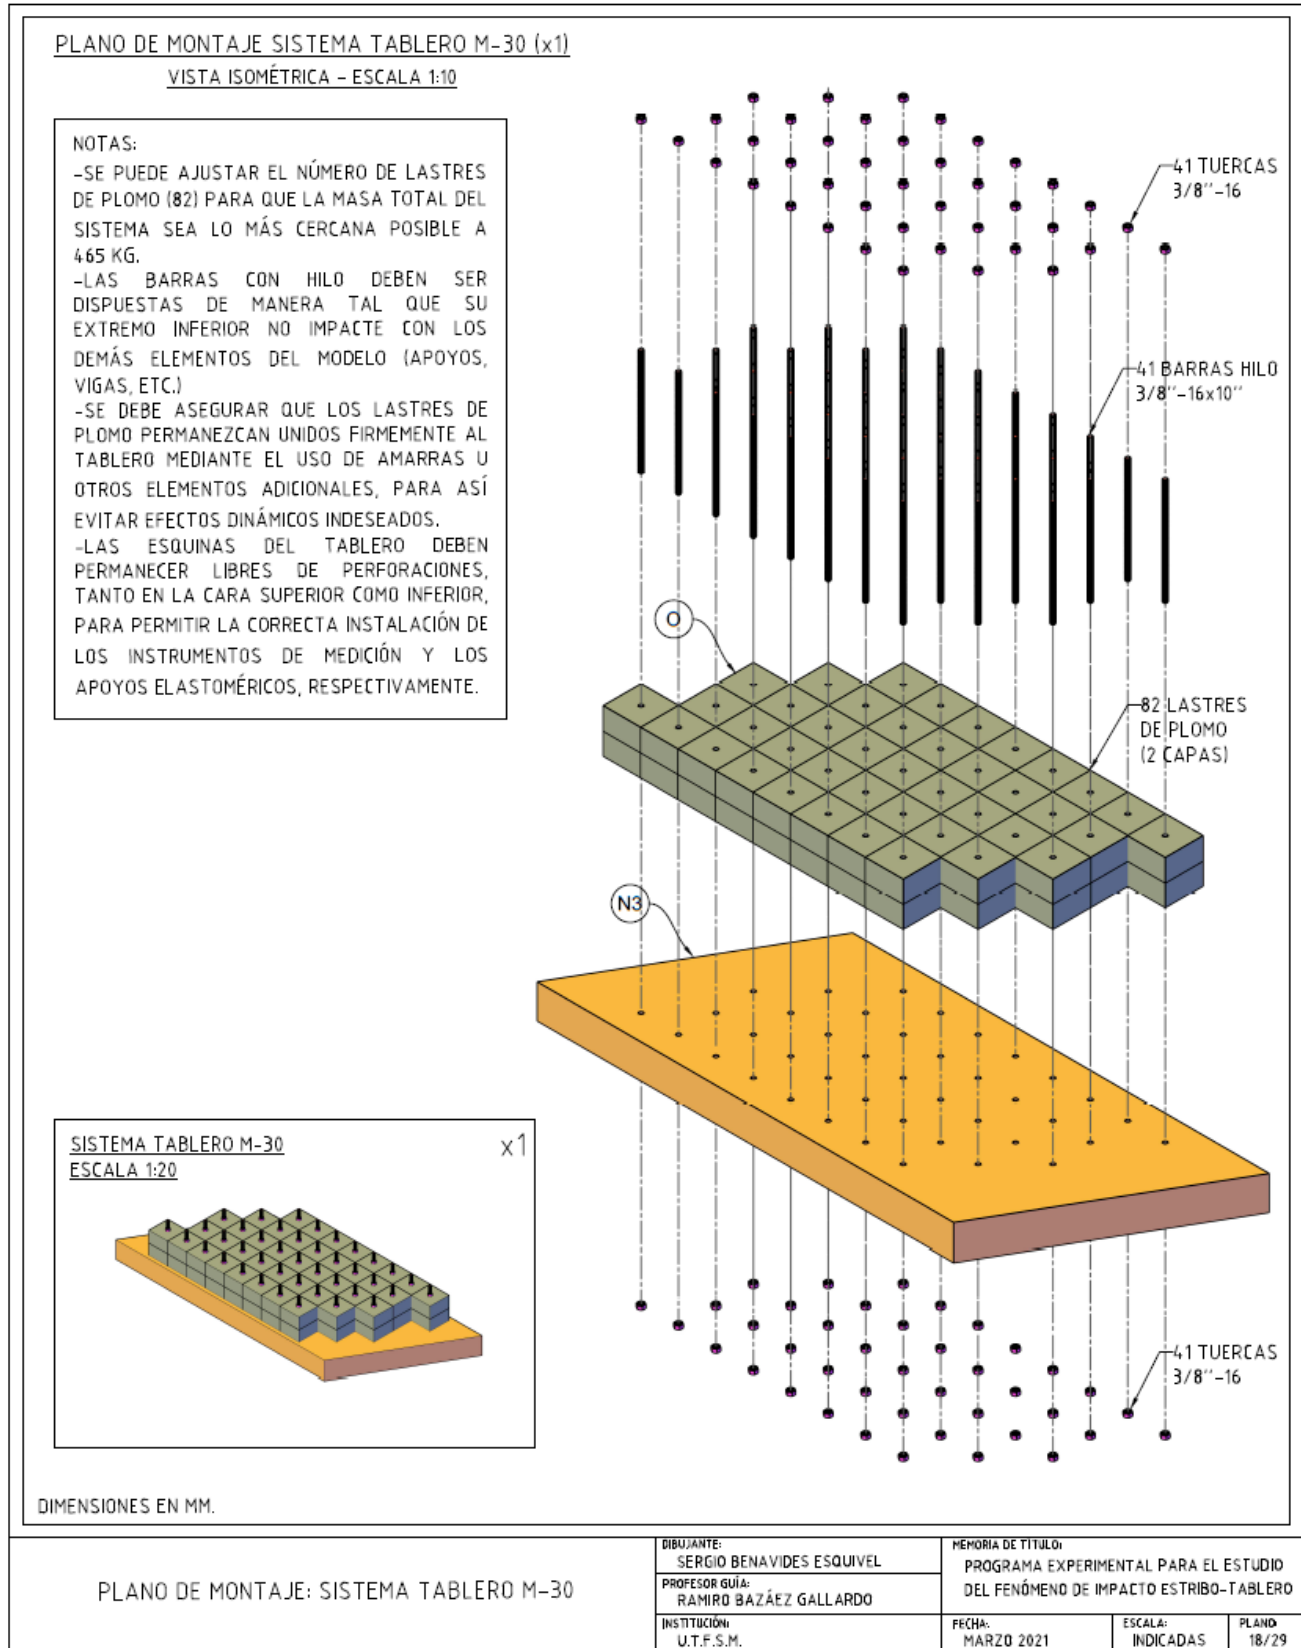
Plano de Montaje: Sistema Tablero M-30.
